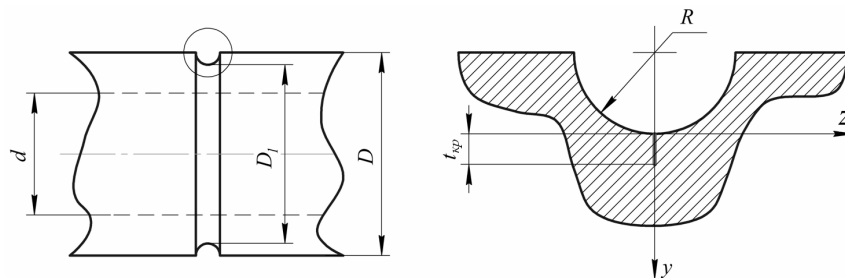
Цилиндрический образец с надрезом и нераспространяющаяся трещина усталости
